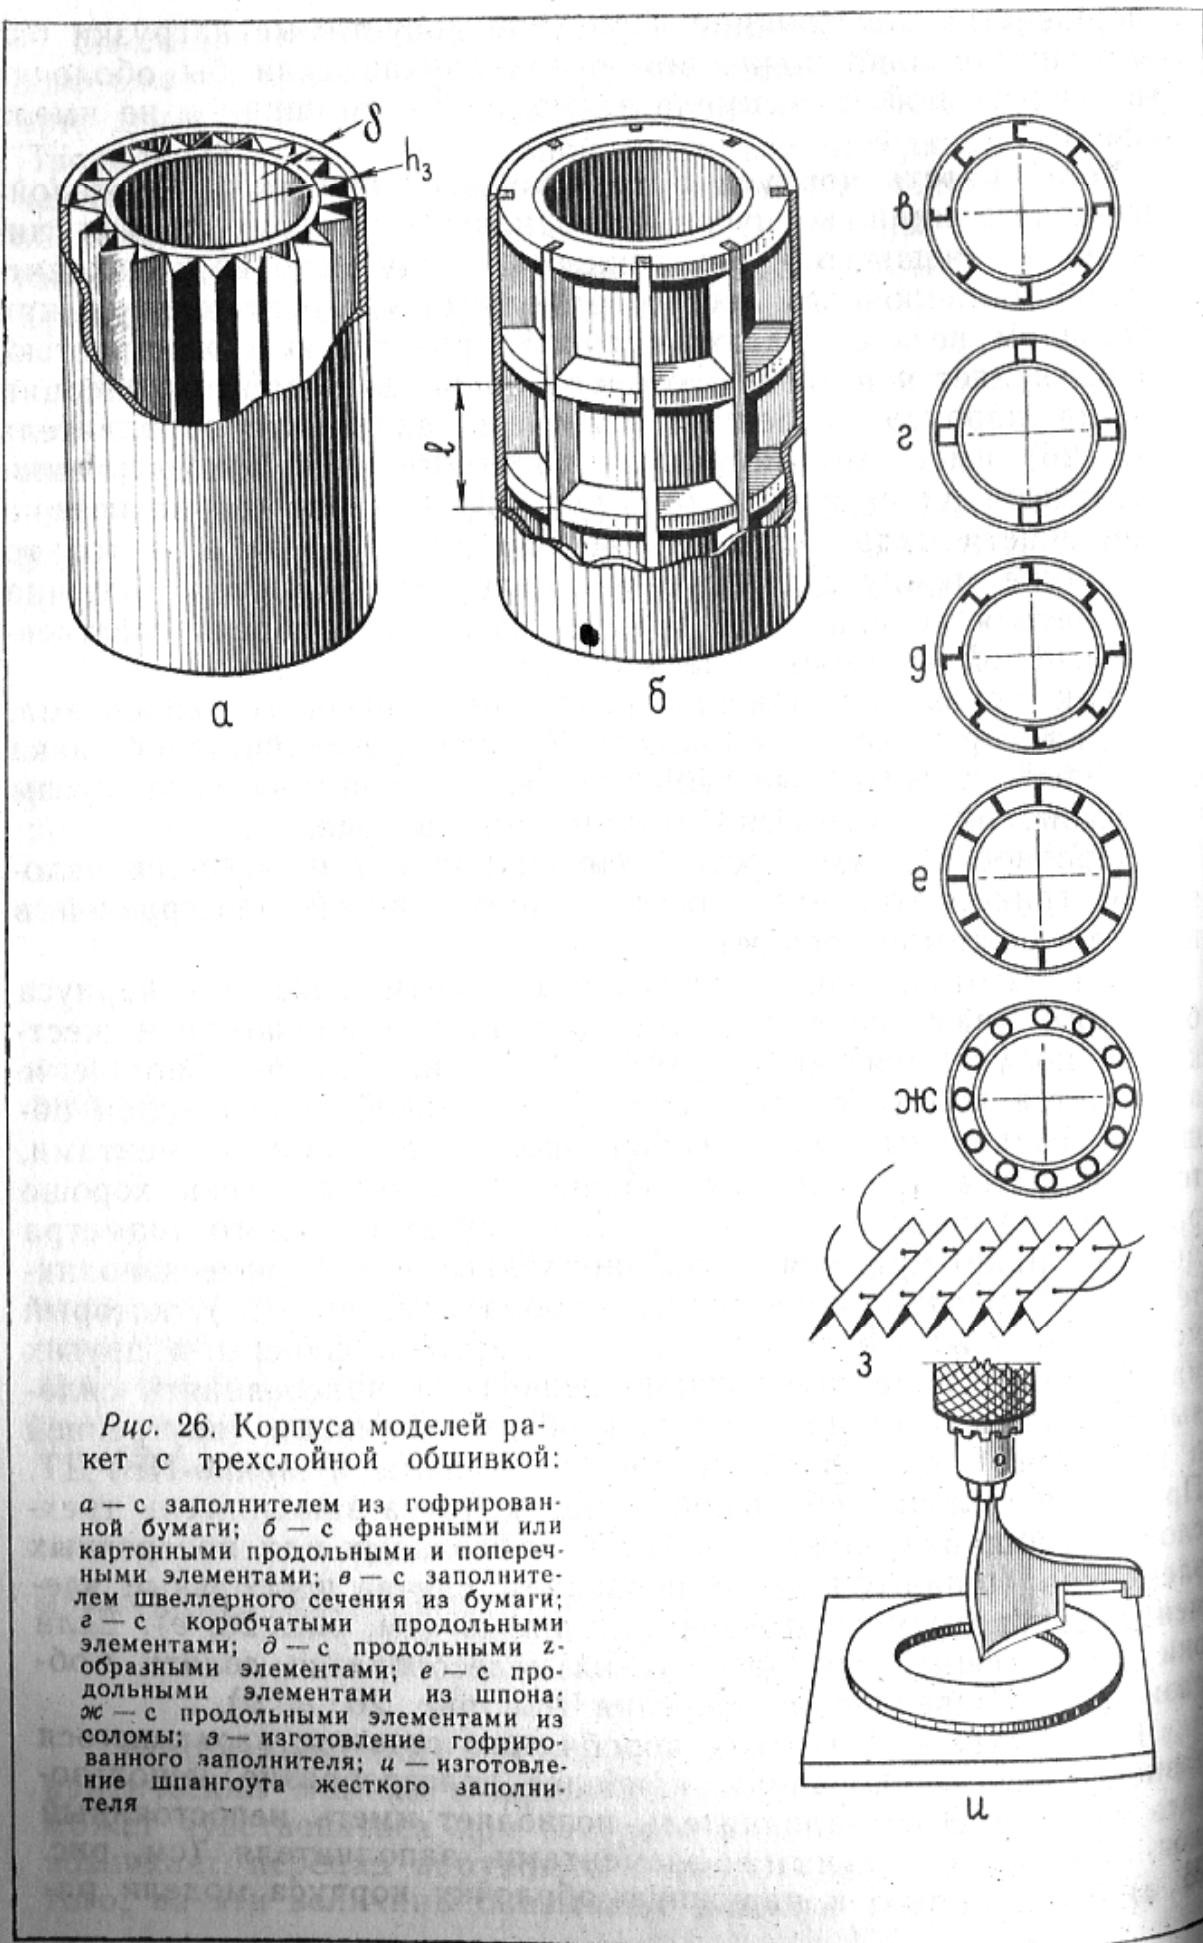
Корпуса моделей ракет с трехслойной обшивкой:
